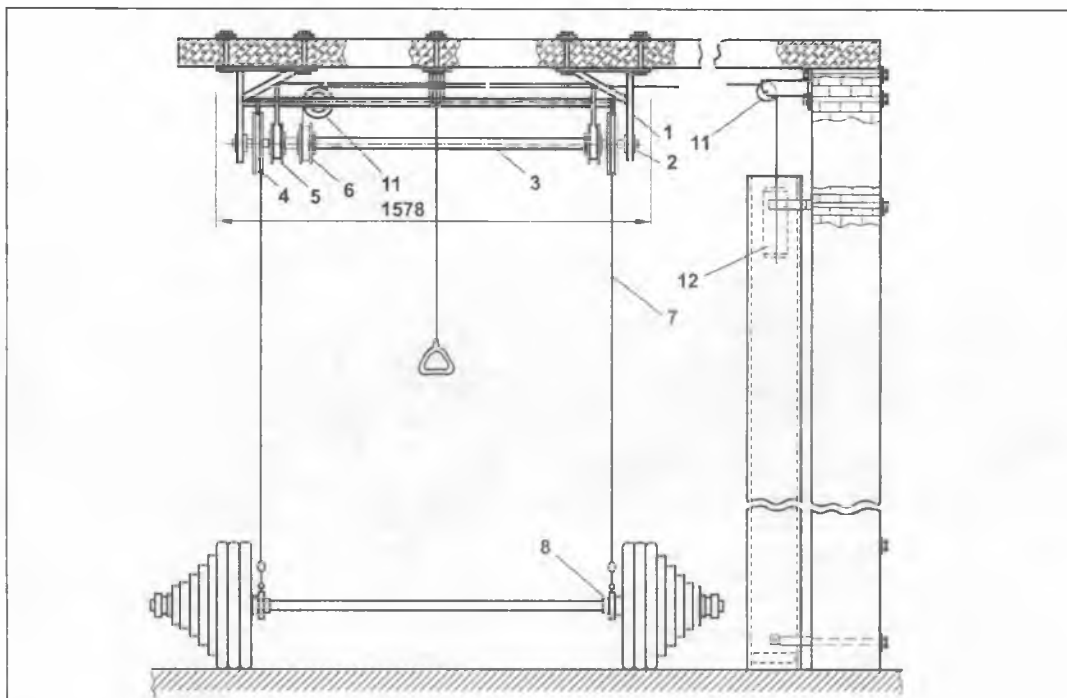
Универсальная установка для тренировки тяжелоатлетов, крепящаяся к потолку
